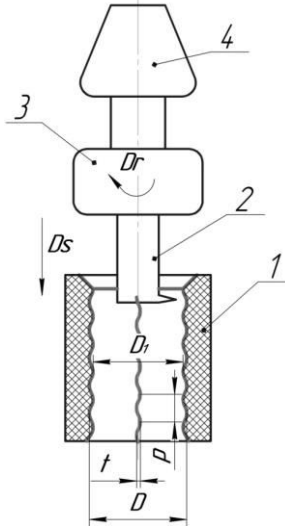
Схема фрезерування круглої різьби в АКМ
